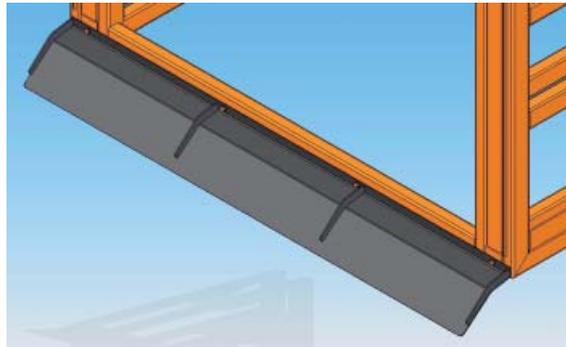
Сыпное устройство подметально-уборочной машины ZMC2.0.
